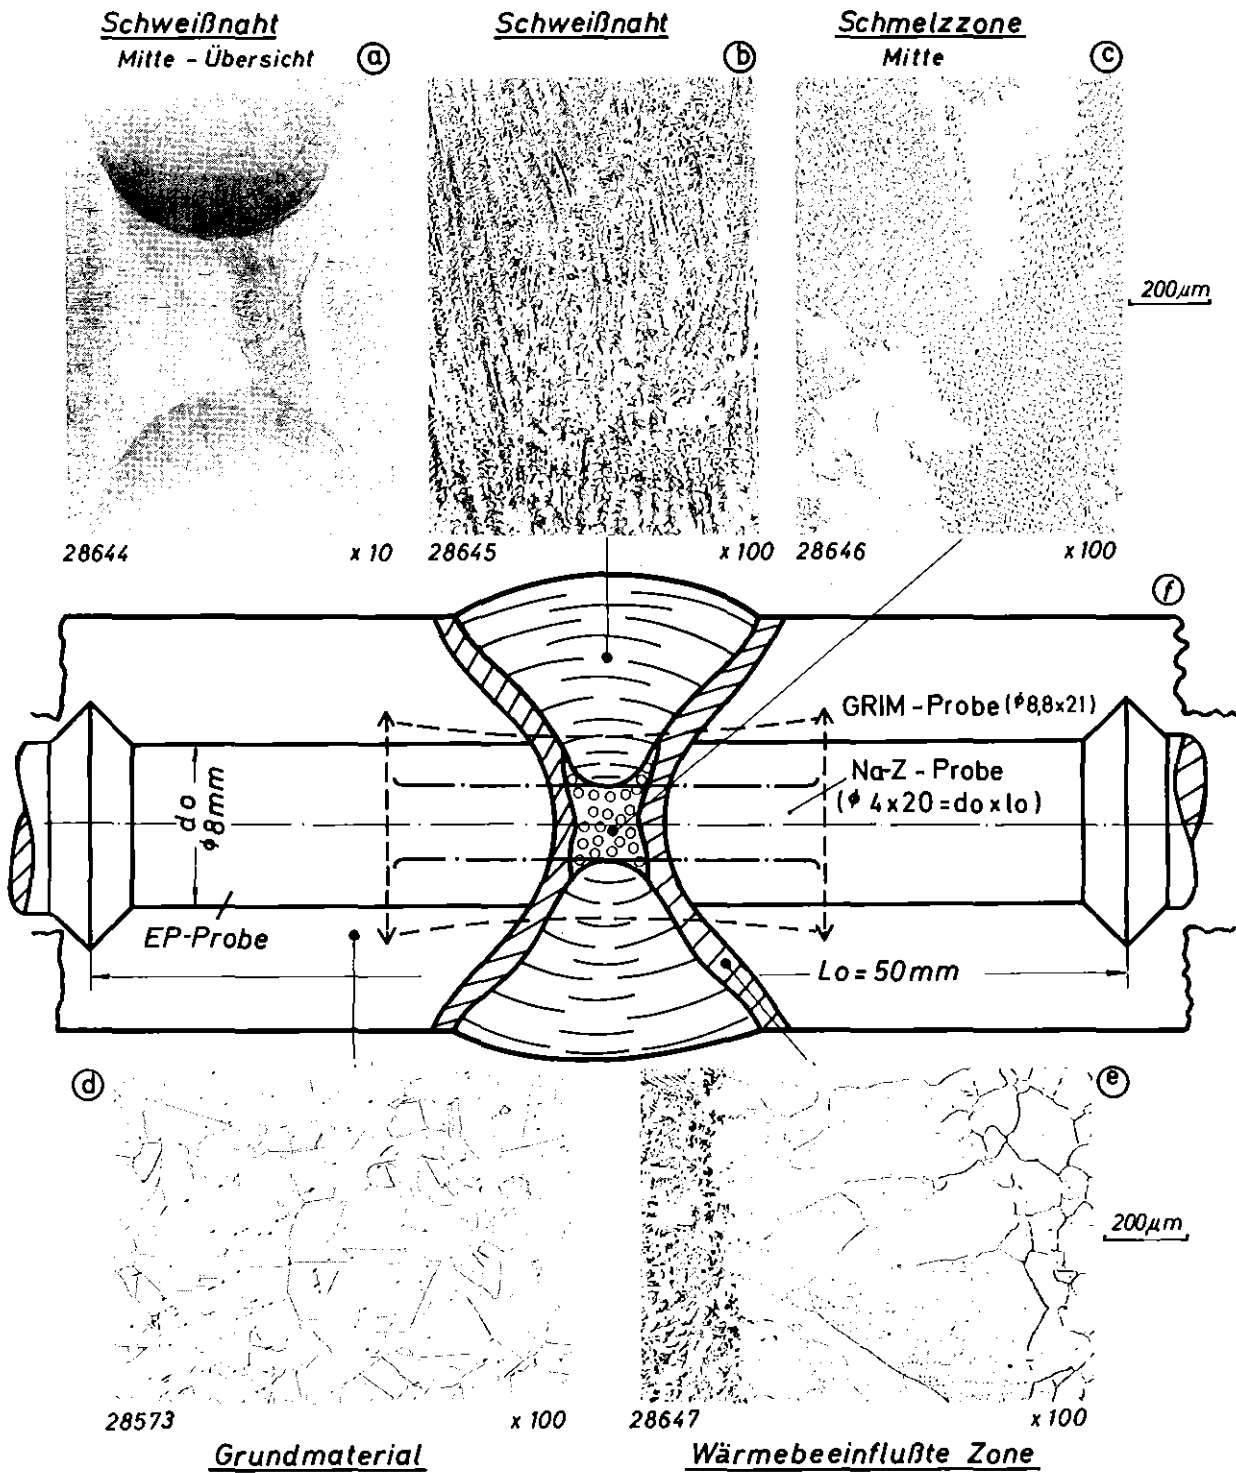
X 6CrNi 1811 (1.4948) Schweißnaht und Probenlage
